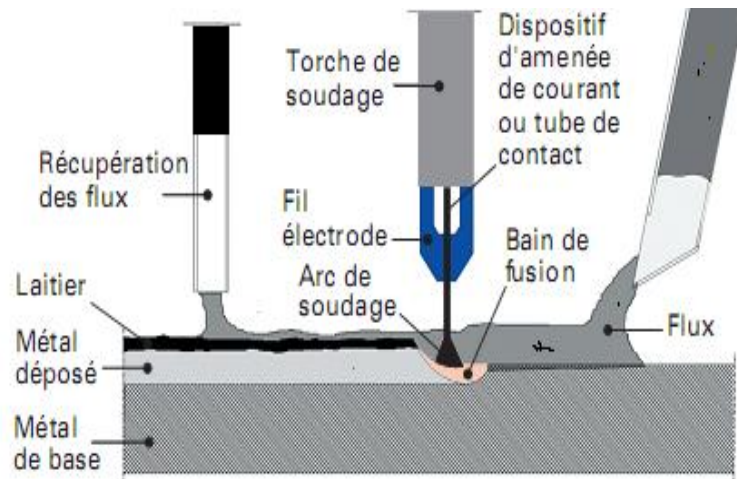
Procédé de soudage à l'arc électrique sous flux solide [2].
